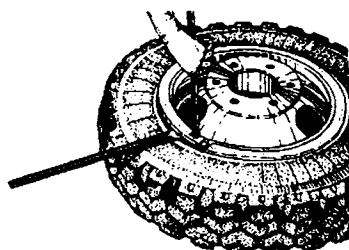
Установка прямой лопатки в прорезь бортового кольца
